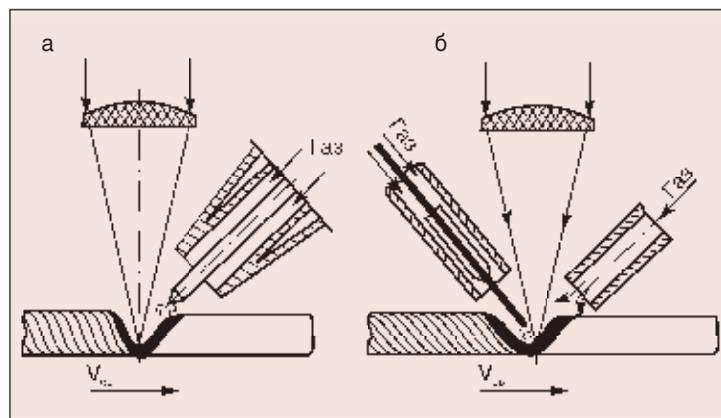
Схема лазерно-дуговой сварки: а — с неплавящимся электродом; б — с плавящимся электродом
